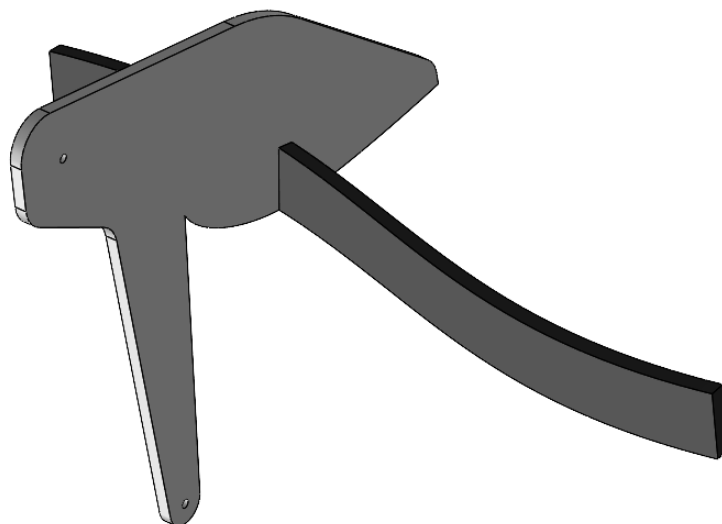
Konstrukcija stražnjeg krila [mm]
